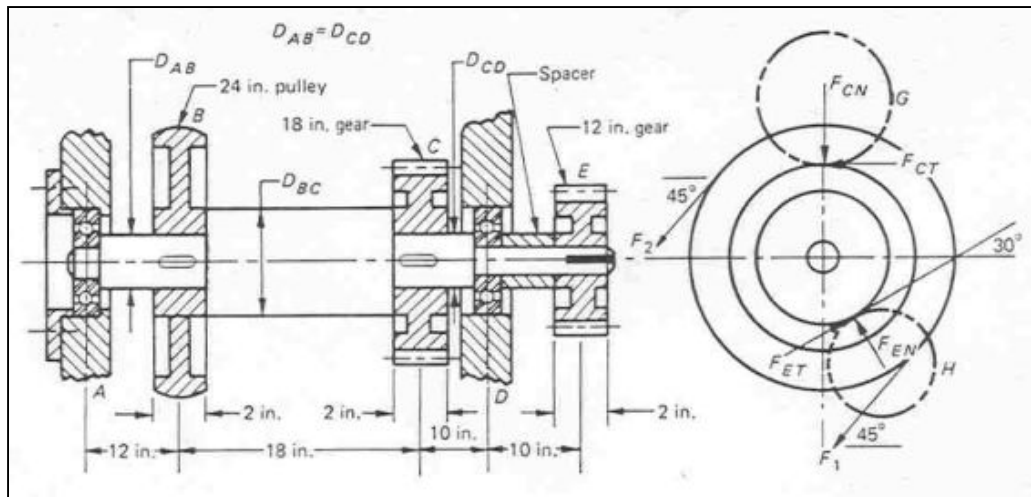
Ensemble de un eje con engranajes y cargas entre sus dientes [3]
